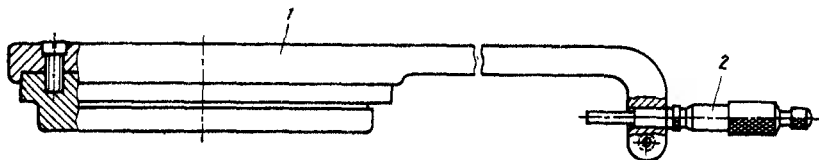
Калибр для проверки радиуса резцов зуборезной головки-протяжки
